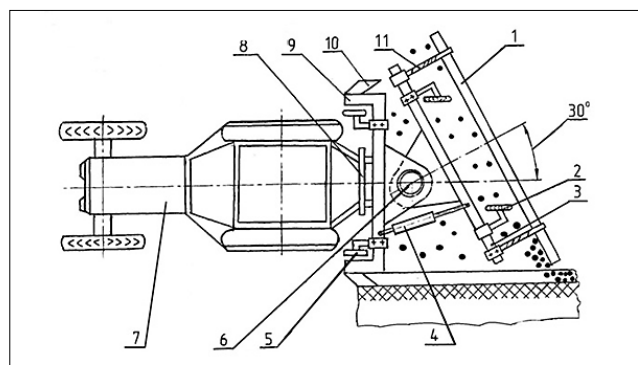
Принципиальная схема агрегата: 1 – гребенка; 2 – опорные колеса гребенки; 3 – подвижная рама; 4 – гидроцилиндр; 5 – опорные колеса плуга; 6 – поворотное устройство; 7 – трактор МТЗ-82; 8 – навесное устройство; 9 – неподвижная рама; 10 – корпус плуга; 11 – пружинные стойки
